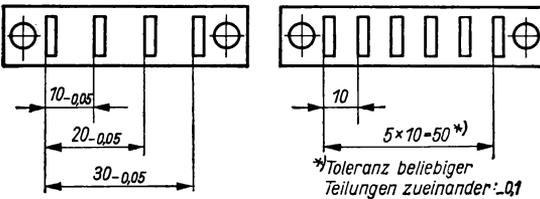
Bemaßung der Lochmitten eckiger Löcher
